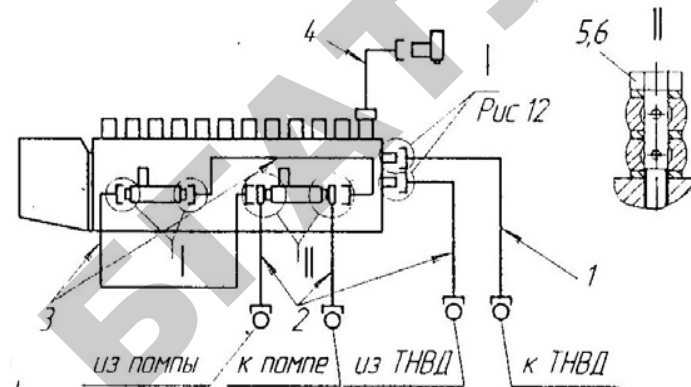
Схема соединения топливопроводов при испытании ТНВД двигателя ЯМЗ-740 со штатным топливоподкачивающим насосом:
